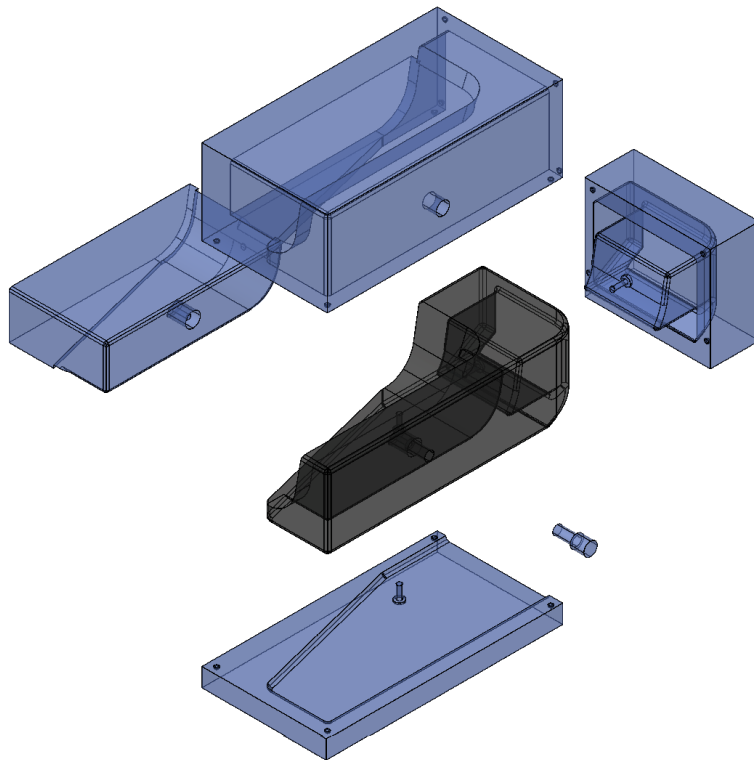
Molde para inyección de la pieza 1.2.6 y 1.1.12
